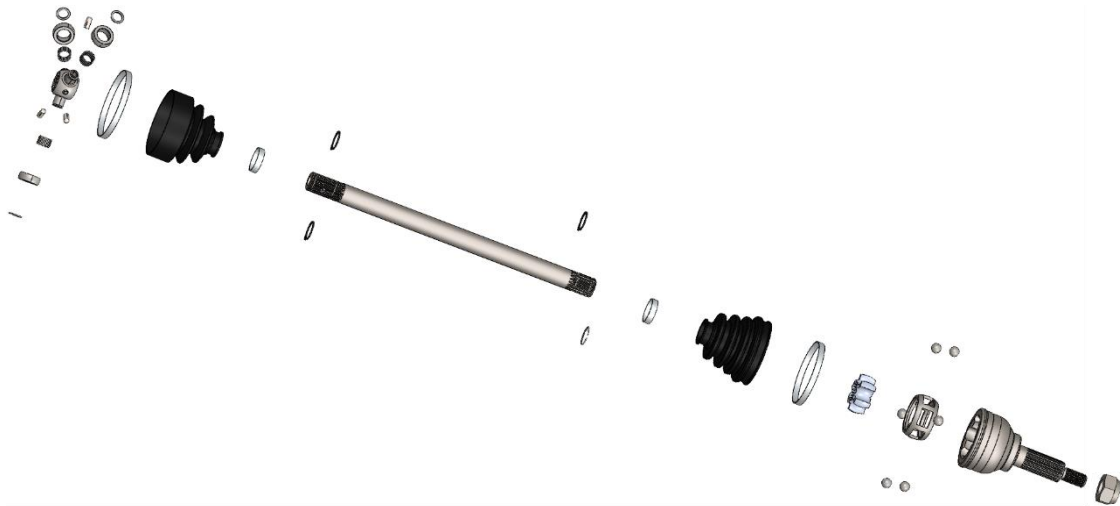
Explosionado subensamblaje del conjunto palier. Elaboración propia.
